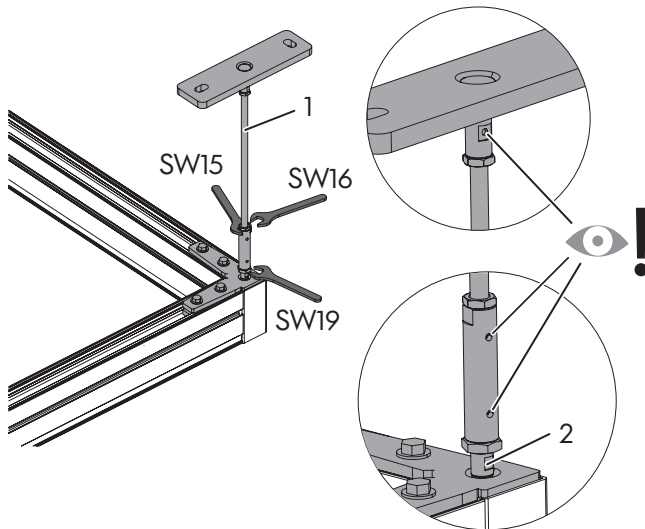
Mit Gabelschlüsseln lockern und Sichtprüfung
